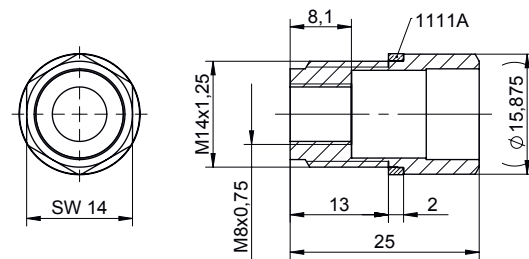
Adapter Typ 6589Q01. Sensor frontbündig
